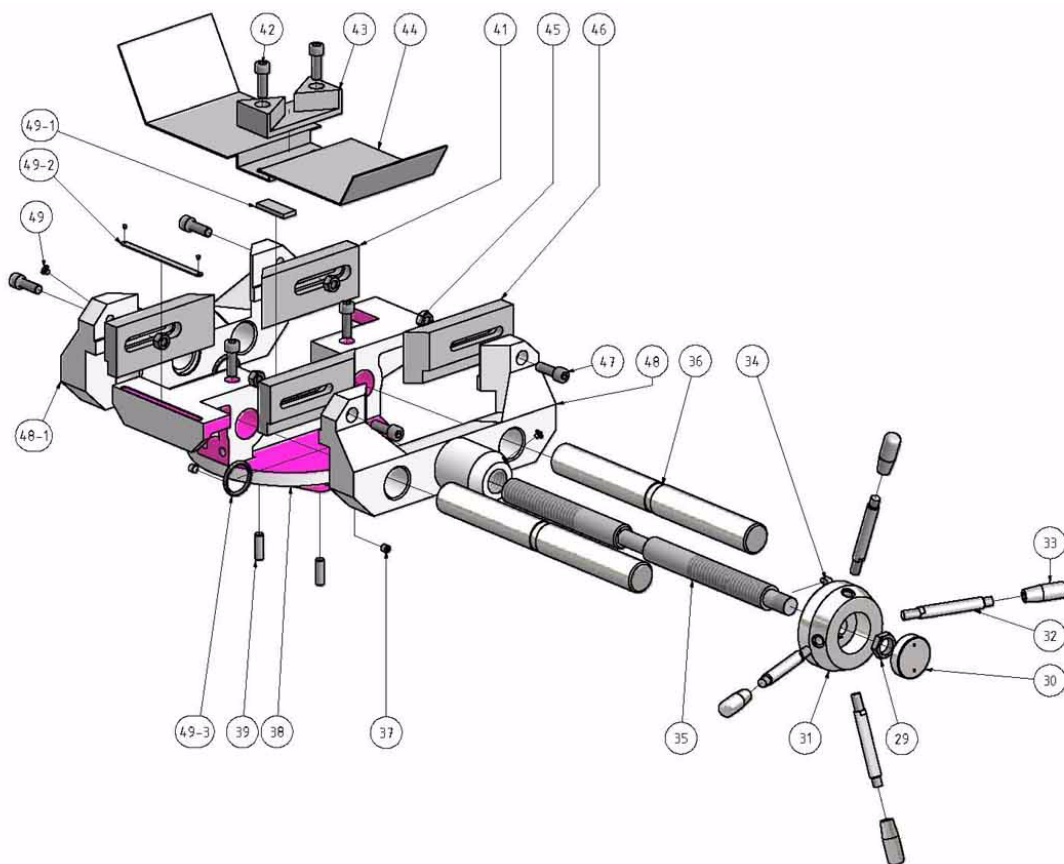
Schnellspannschraubstock - Machine vice - CS275/ CS315
